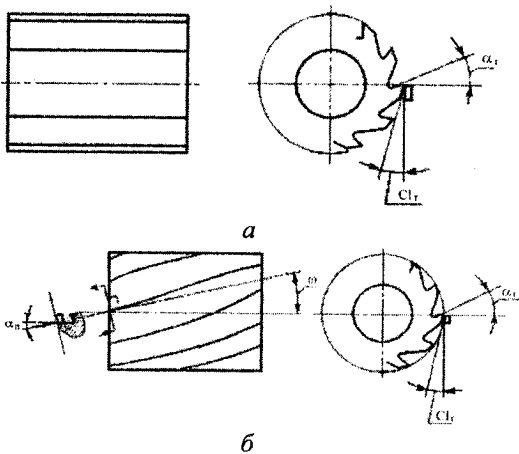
Схема фрез з прямим (а) і гвинтовим (б) зубами
